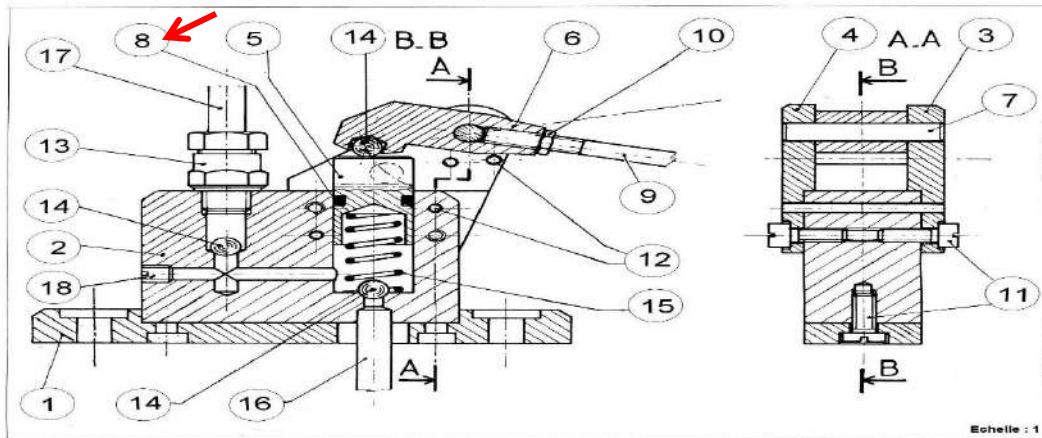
Dessin d'ensemble de pompe hydraulique manuelle
